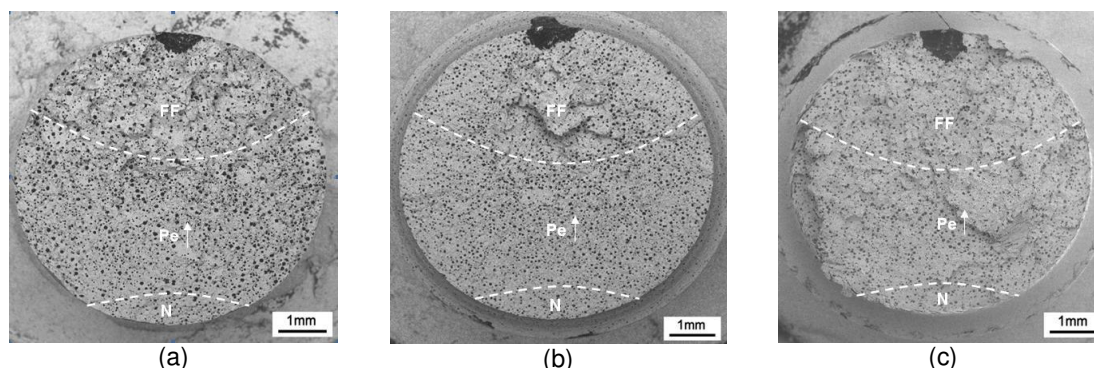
Aspecto macrográfico das superfícies de fratura dos corpos de prova: (a) sem entalhe, (b) com entalhe, e (c) com entalhe roleteado, obtidas pela técnica de elétrons retro-espalhados
